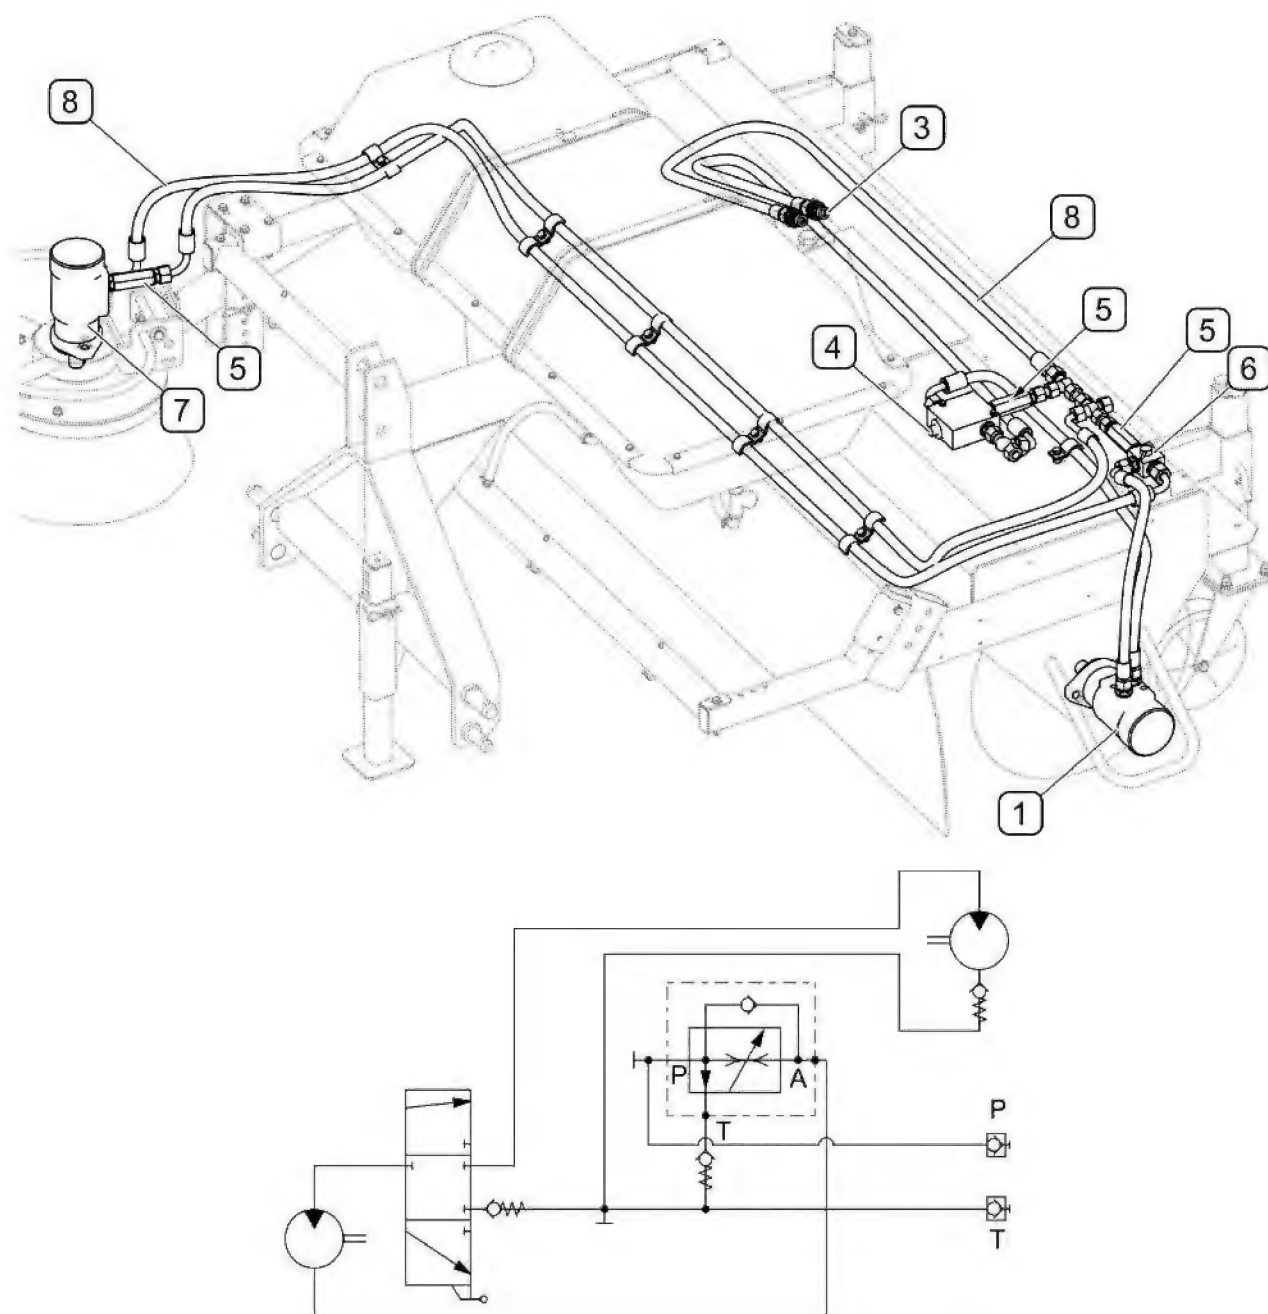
A Construction du circuit hydraulique de la balayeuse ZM-1600-04
